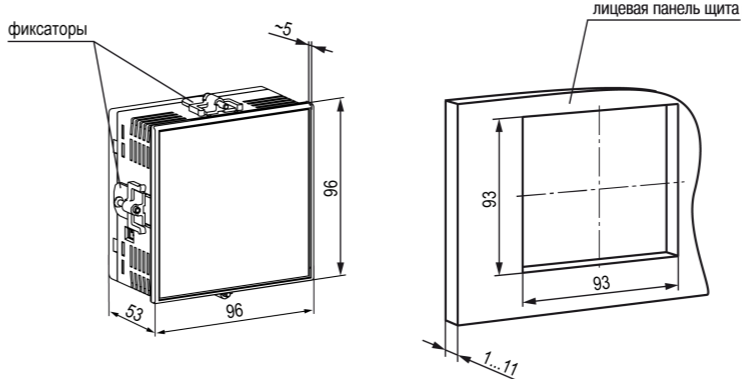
Габаритные размеры корпуса Щ1 и монтажного отверстия в щите лицевая панель щита
